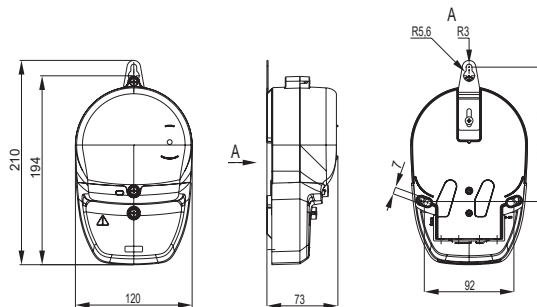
Габаритные и присоединительные размеры счетчиков типа TE102
